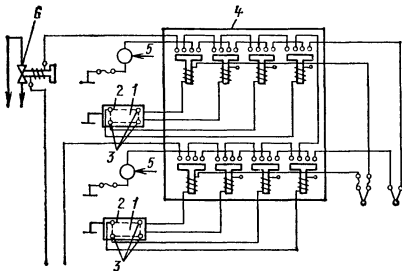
Схема электроконтактного контроля точности позиционирования детали в приспособлении (по четырем точкам):
